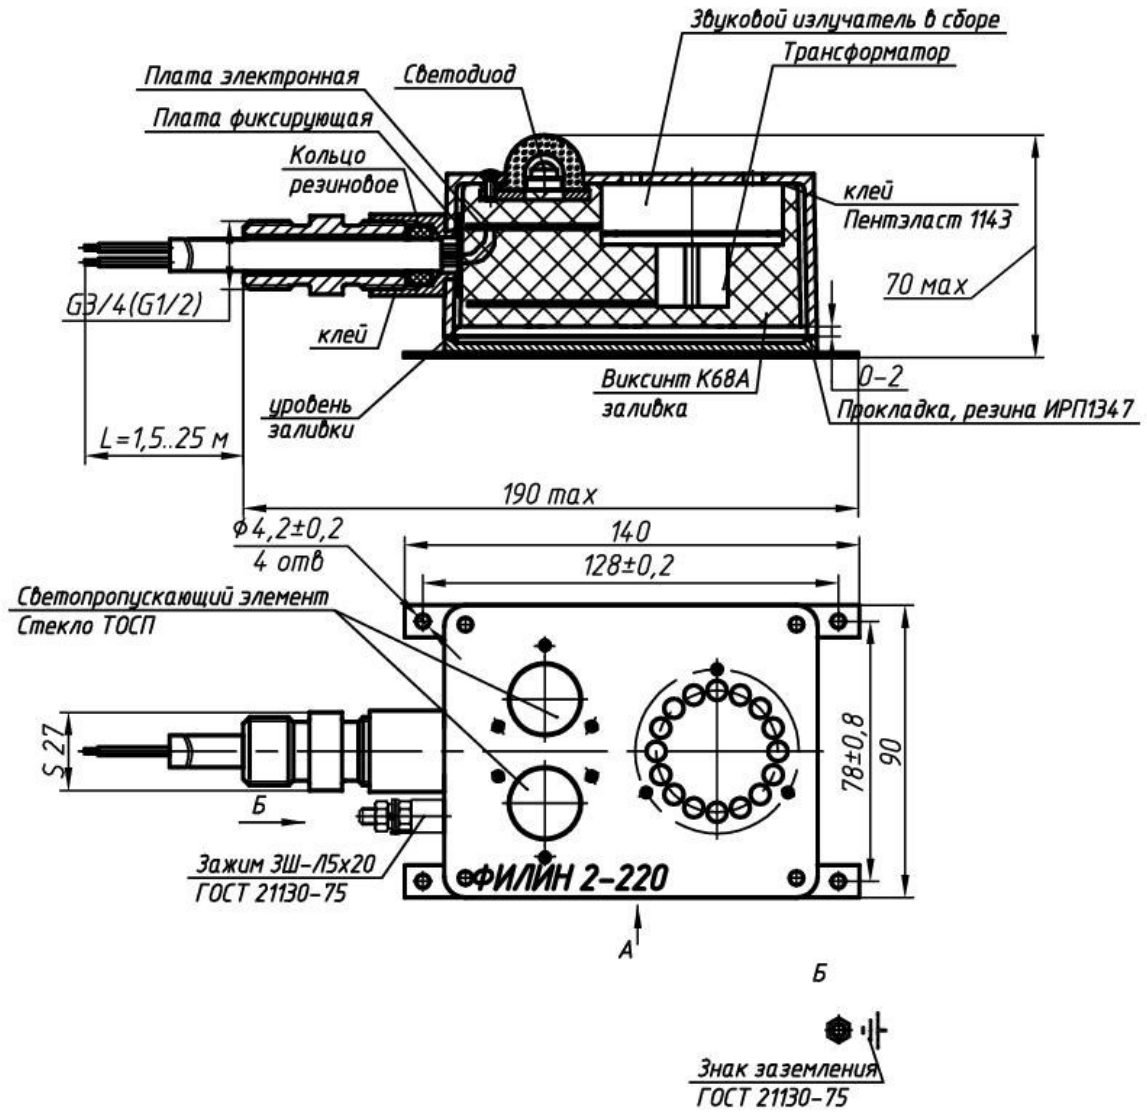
б – Габаритный чертёж оповещателей Филлин-2-220, совмещённый с чертежом средств взрывозащиты
